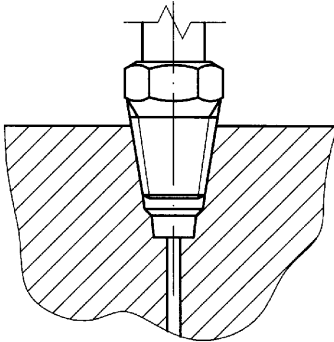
Kegelige Gewinde, Abdichtung im Gewinde
